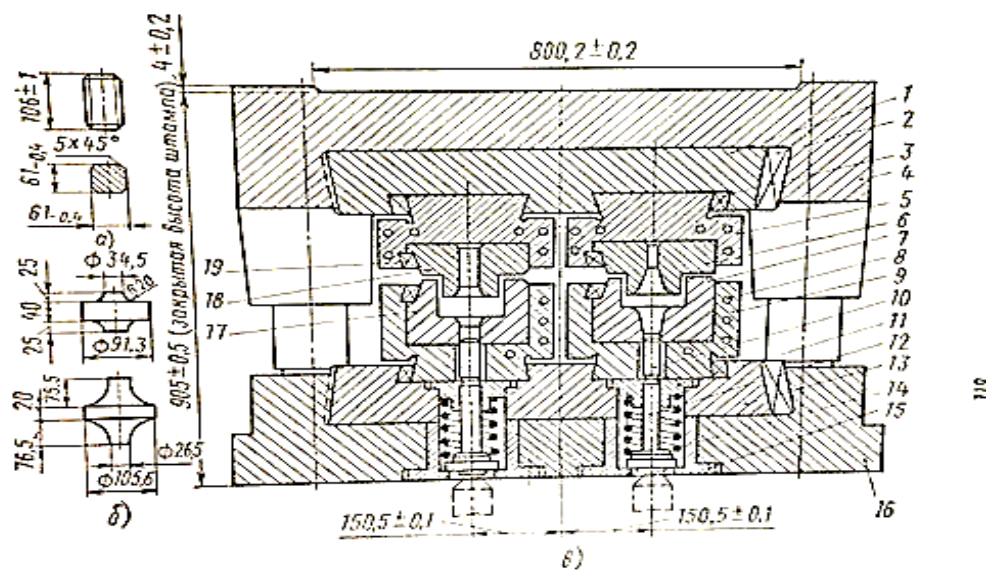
Заготовка (а), переходы штамповки (б) и штамп для выдавливания поковки диска турбины (в):
